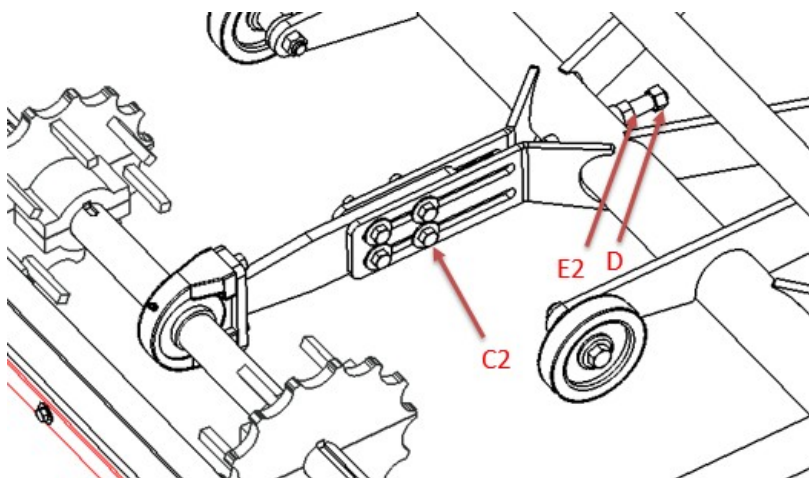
Центральный опорный кронштейн приводного вала подъемного транспортера
